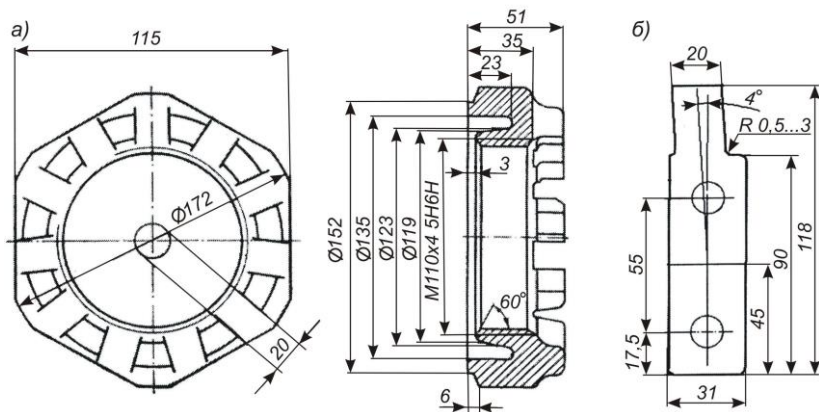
Элементы торцевого крепления подшипников на шейке оси типа РУ1:
